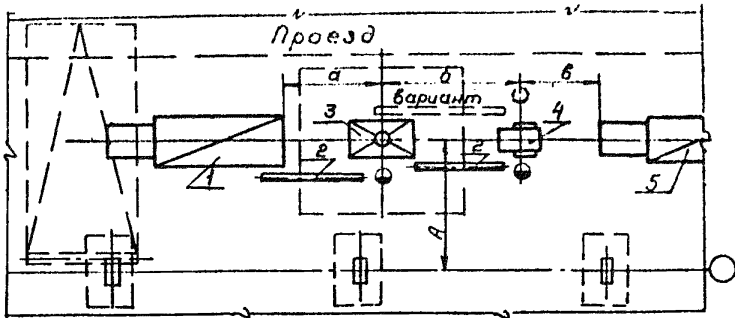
Схема расположения штамповочных линий на базе ПИМ:
